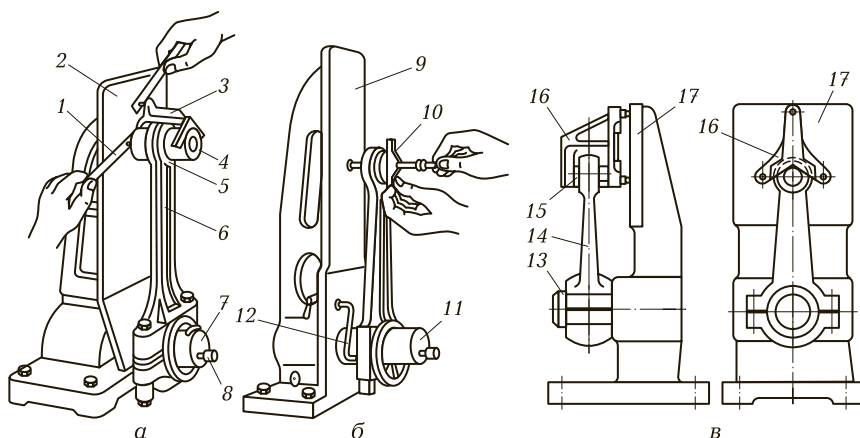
Контроль сборки шатуна выполнением проверок:
